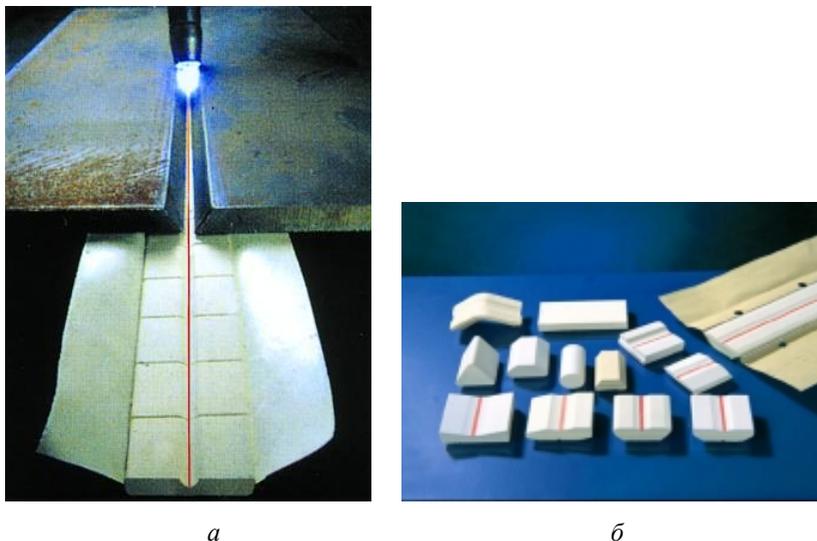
Схема сварки на съемной подкладке:
